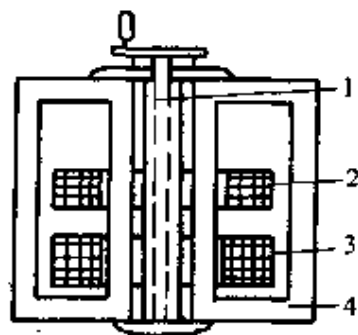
动圈式系列交流电焊机结构示意图
